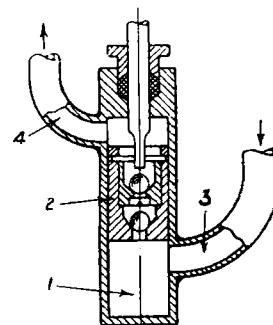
Kolben-Rückpumpe mit Kugelventilen.
